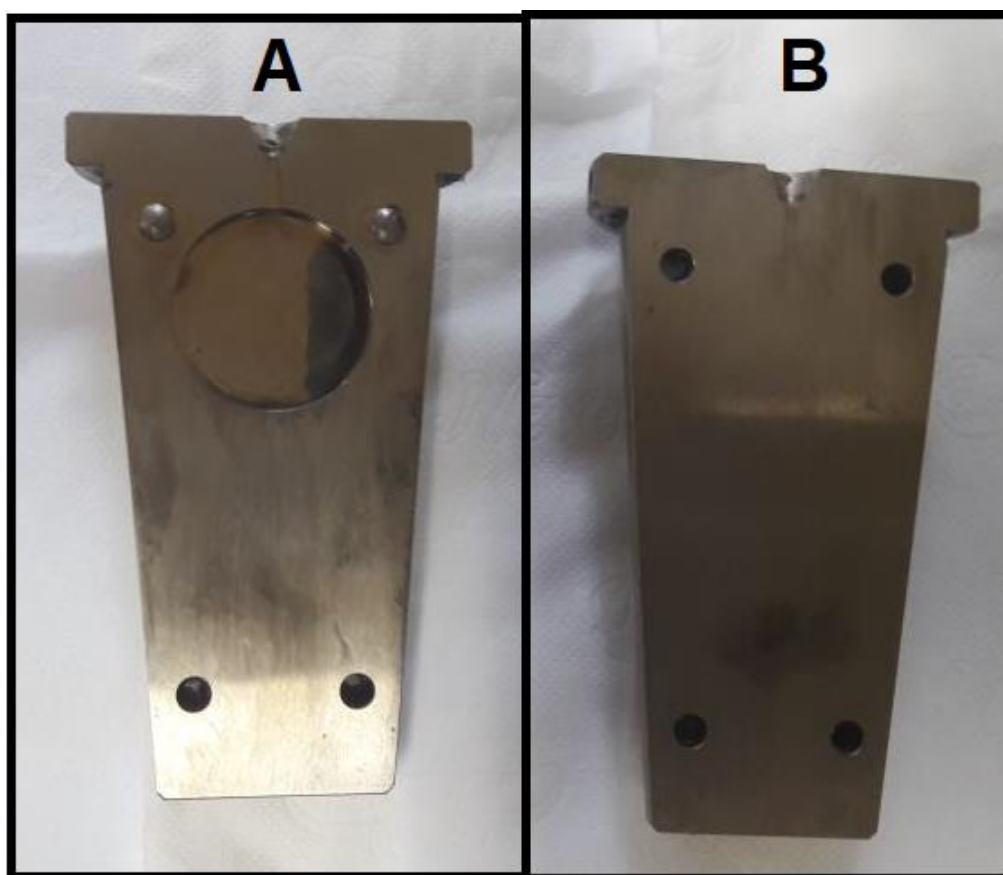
Molde cônico utilizado como modelo para produção dos moldes tubulares, A- Face fêmea; B- Face macho.
